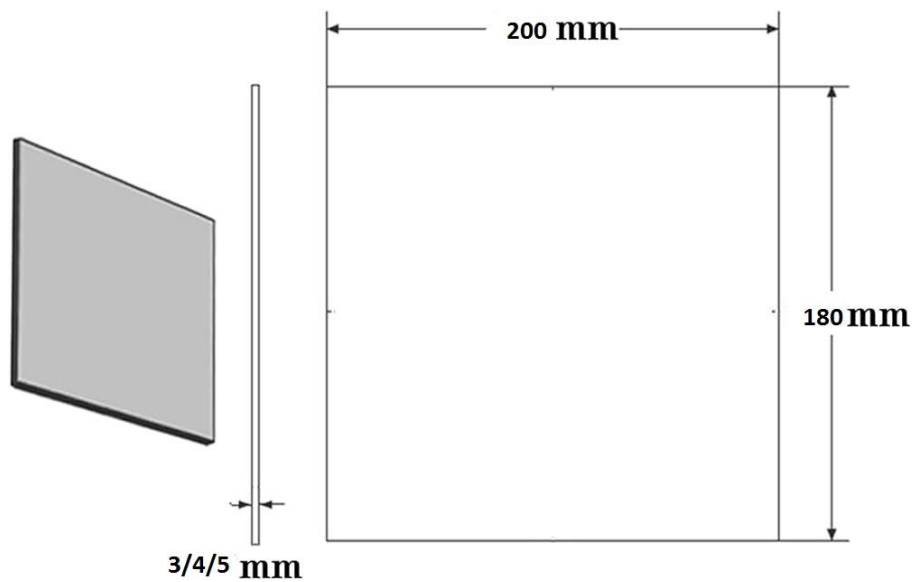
illustration des dimensions des plaques de tôle utilisée
